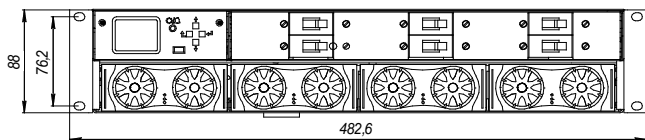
Габаритный чертеж УЭПС-5К 60/120-0404-1УТ
